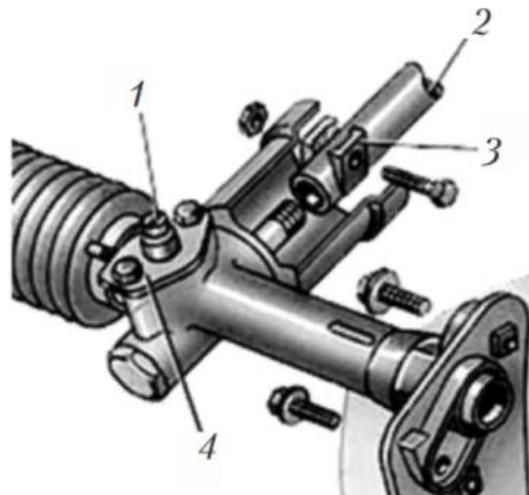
Рулевое управление реечного типа автомобиля Audi: 1 — регулировочный винт; 2 — нижний вал колонки рулевого управления; 3 — хомут; 4 — крышка
